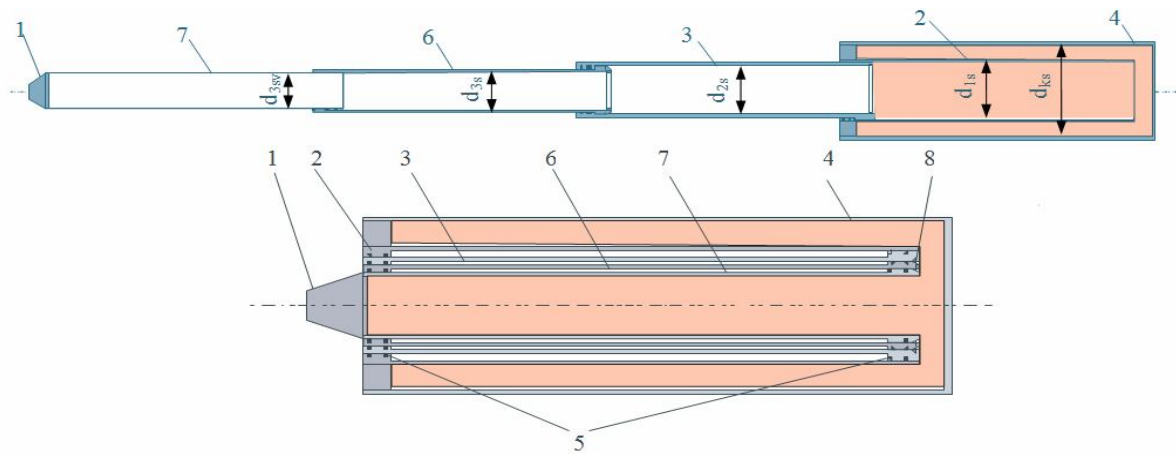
Схема трехступенчатого пневмоцилиндра с ресивером 1 – узел крепления к каретке, 2 – корпус пневмоцилиндра, 3 – цилиндр первой ступени, 4 – ресивер, 5 – узлы уплотнения, 6 – цилиндр второй ступени, 7 – цилиндр третьей ступени, 8 – стопорное кольцо
